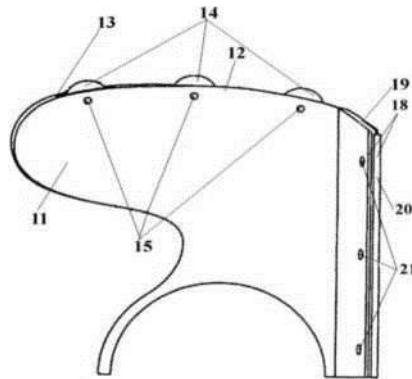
Лопасть-нож смесителя (вид сбоку): 11 - лопасть; 12 - верхняя поверхность лопасти; 13,19 - паз; 14,20 - нож; 15 - 21 - винт; 18 - передняя поверхность лопасти.
